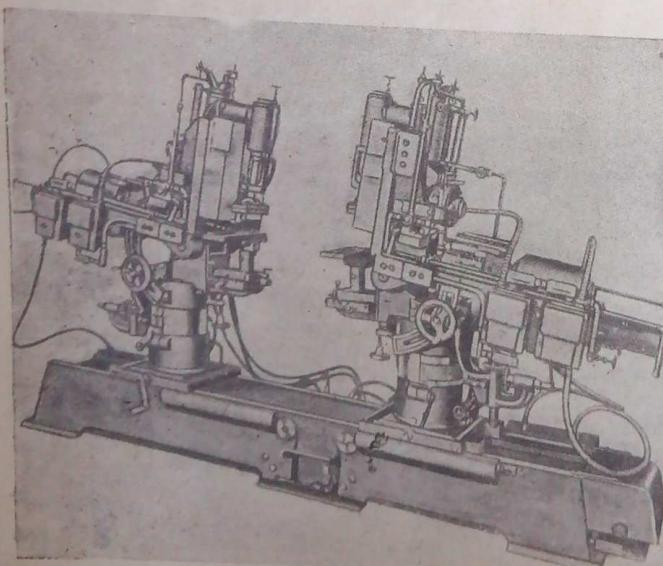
Двусторонний торцово-сверлильный автоматический станок
